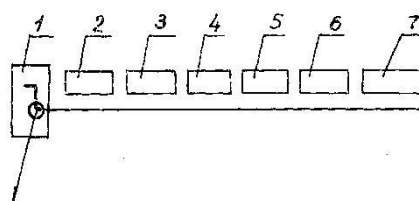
Структурная схема обозначения сварных швов на чертежах по ГОСТ 2.312-72
